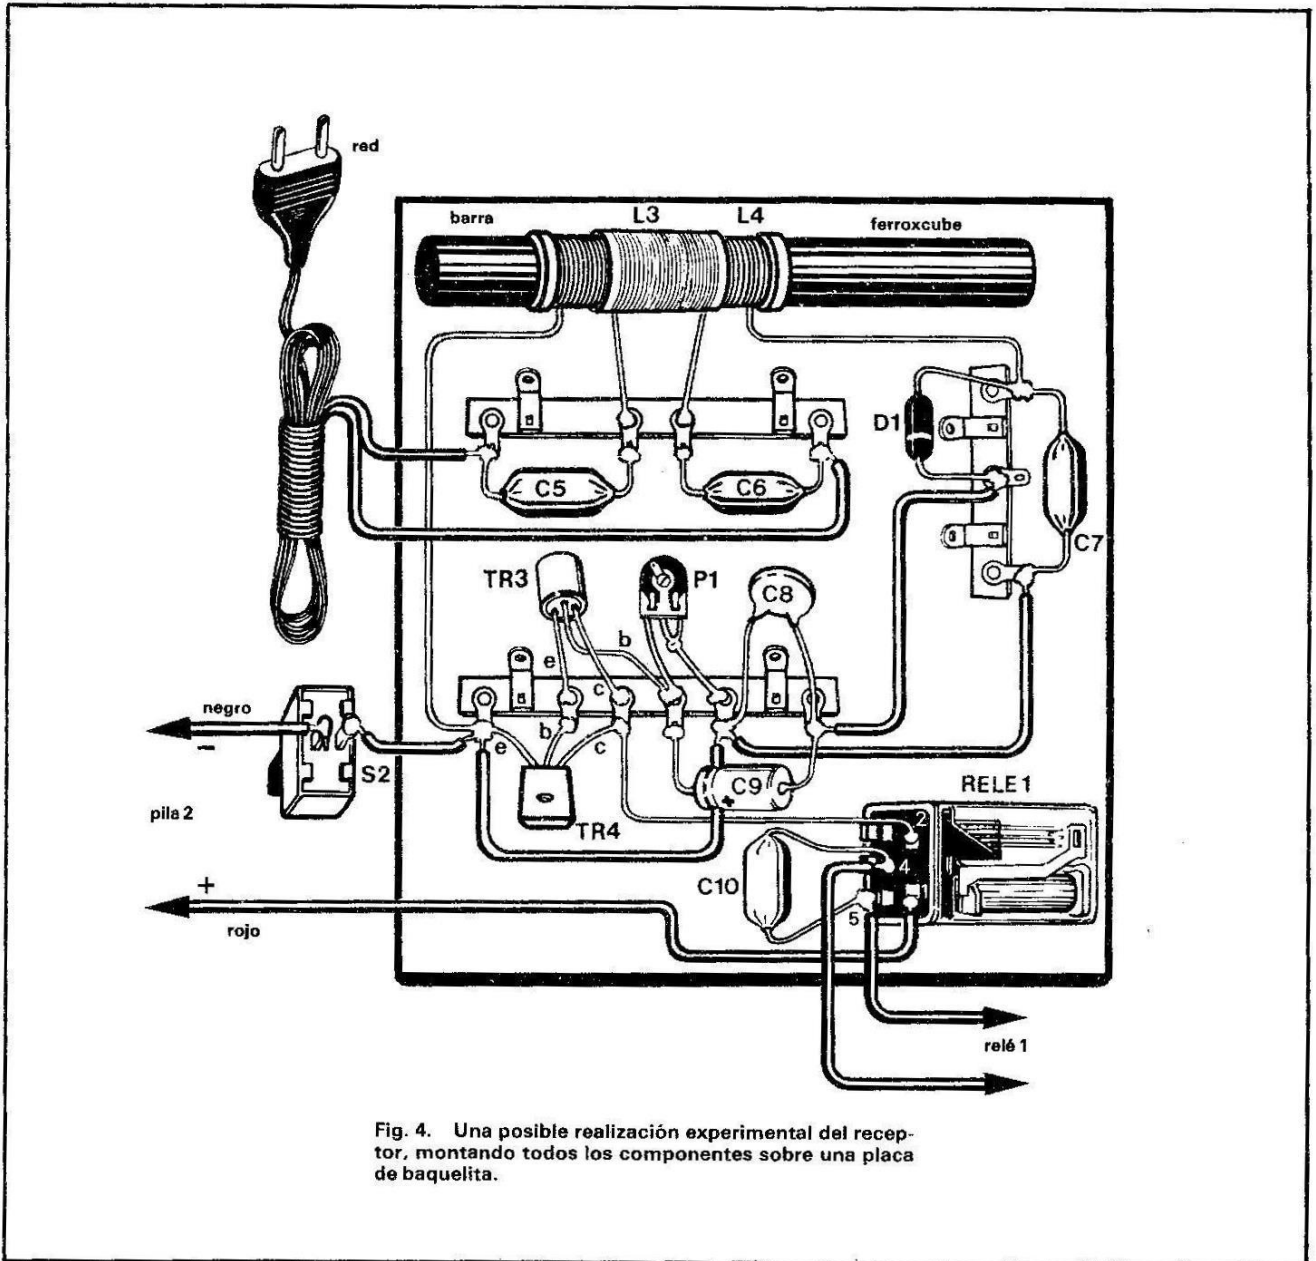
Una posible realización experimental del receptor, montando todos los componentes sobre una placa de baquelita.
